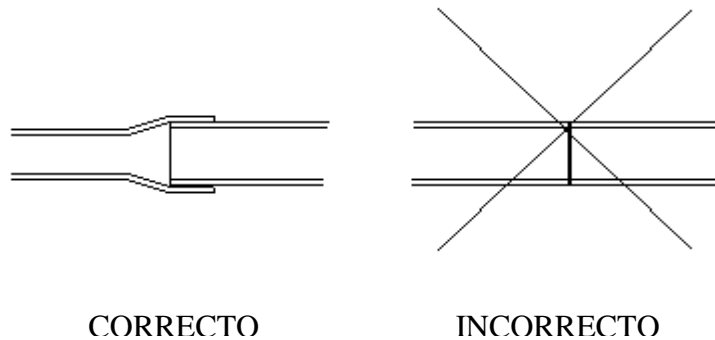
SOLDADURA DE TUBERÍA DEL MISMO DIÁMETRO.
